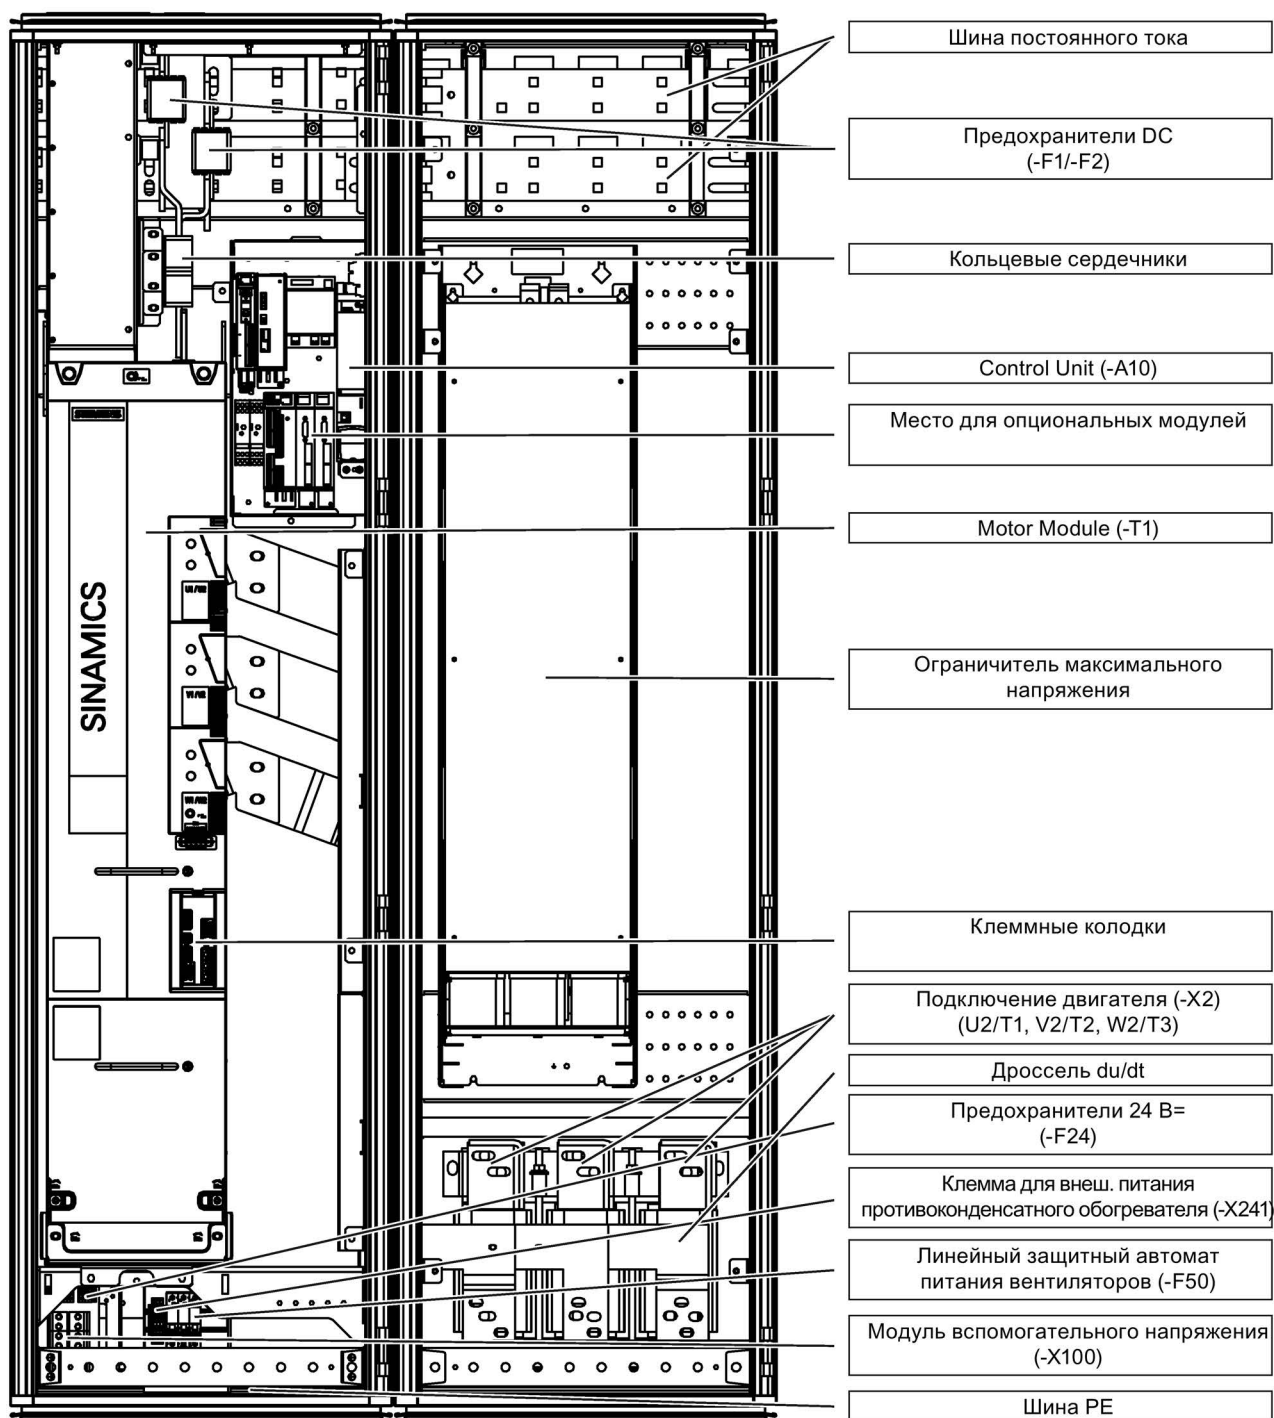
Пример сборки модуля двигателя – формат «шасси-2» (типоразмер FS4) с опцией L10
